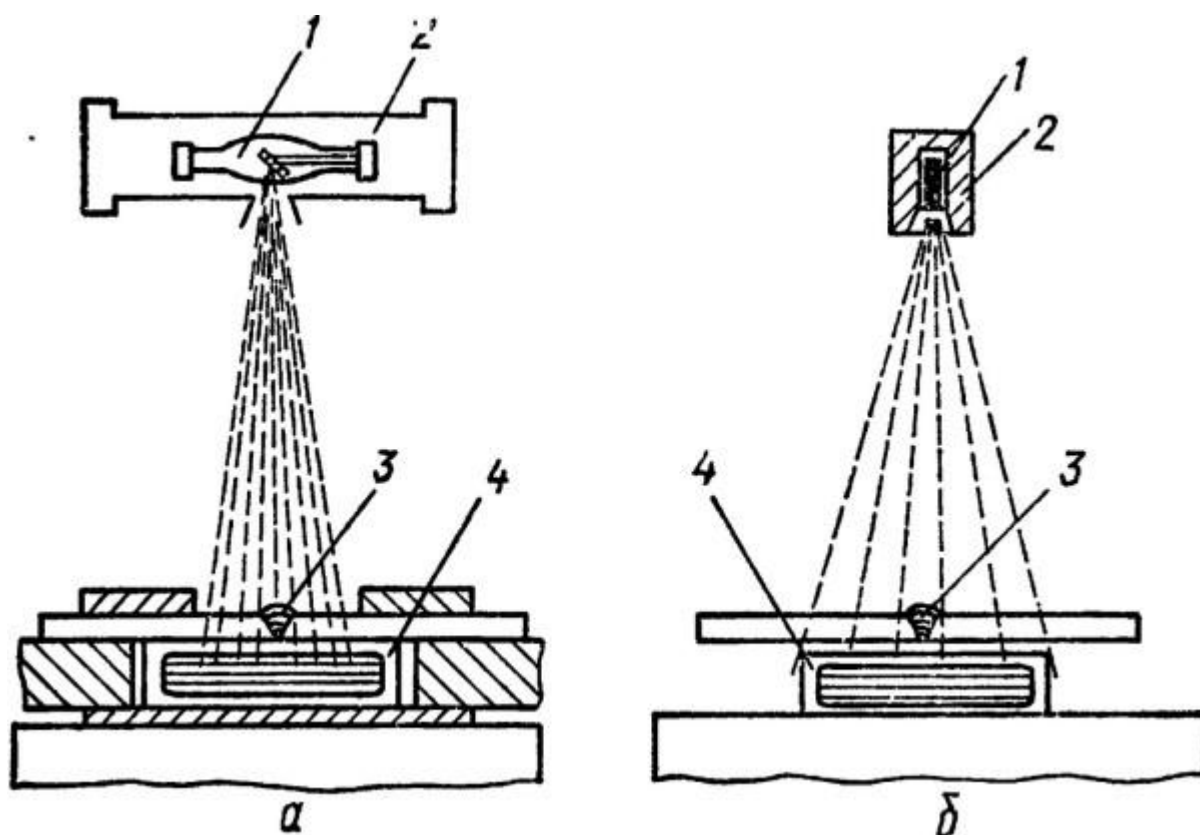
Радиационный контроль: 1 - лампы; 2 - контейнеры; 3 - сварной шов; 4 - пленка
